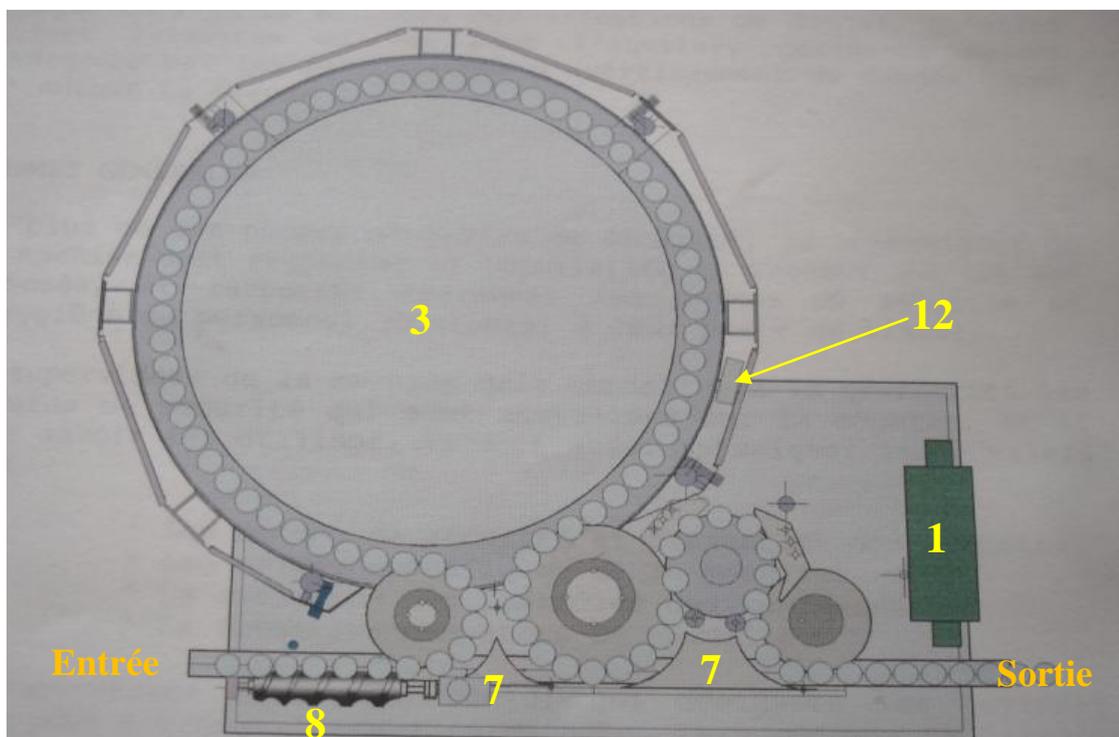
Vue de haut de la remplisseuse MONOBLOC [10].
